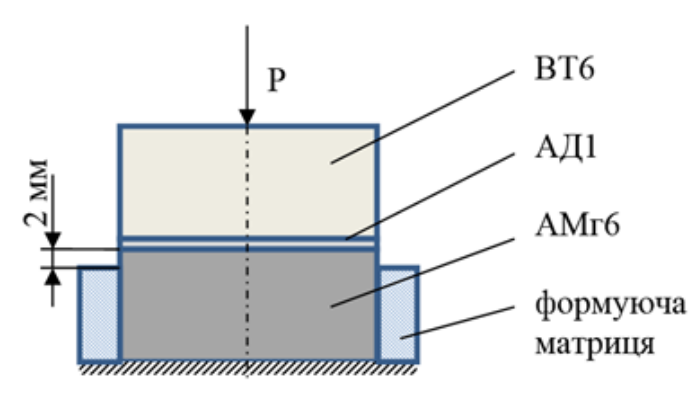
Схема зварювання з використанням формуючої матриці
